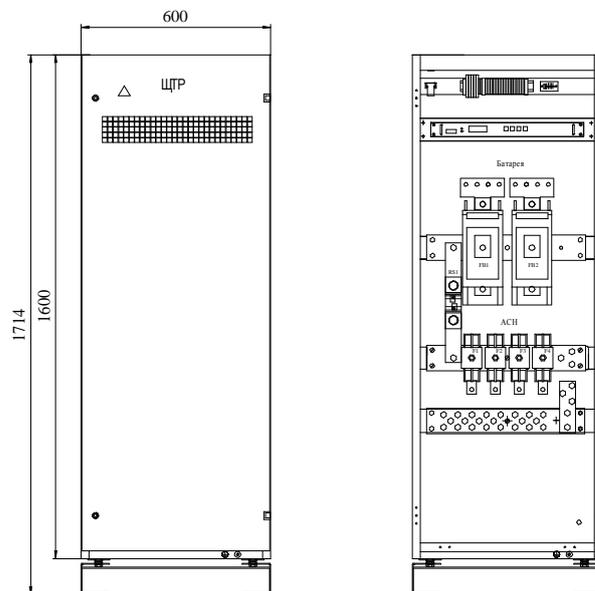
Габаритный чертеж ЩТР-4-В (глубина стойки 600мм)
